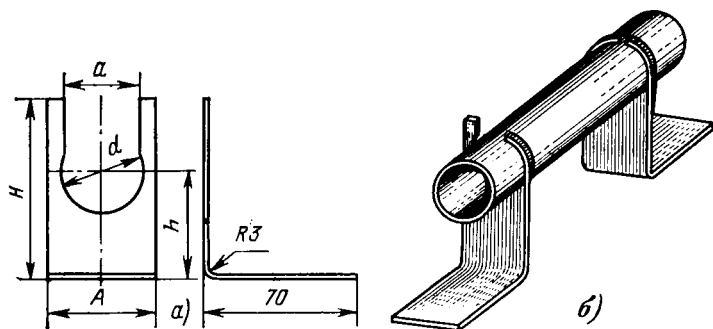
Скоба для неподвижного крепления пластмассовых труб:
